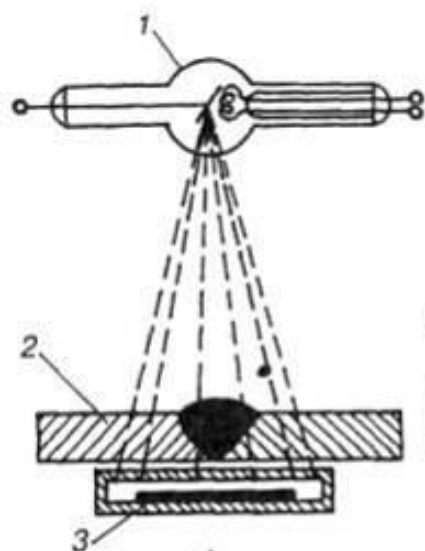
Схема радіографічного контролю зварного з'єднання: 1 – джерело випромінювання; 2 – зразок; 3 – чутлива плівка
